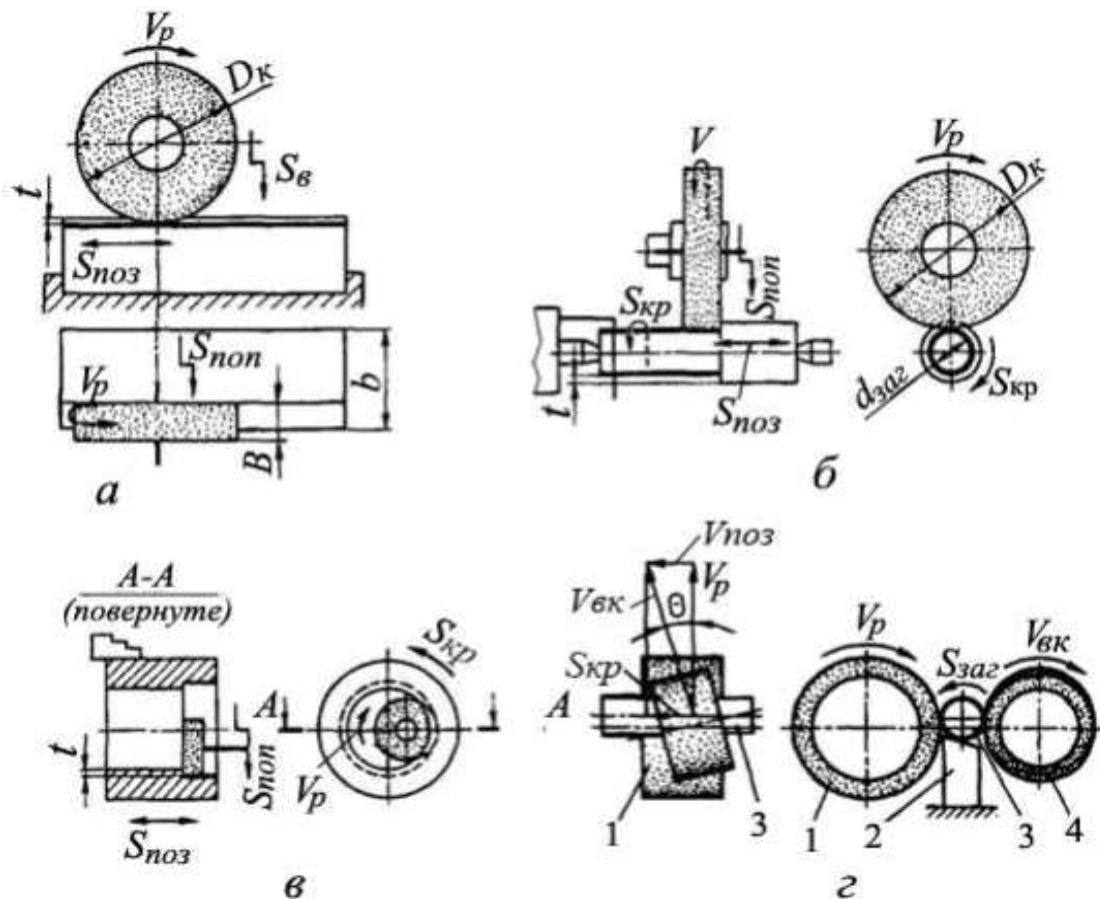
Схеми обробки на шліфувальних верстатах
